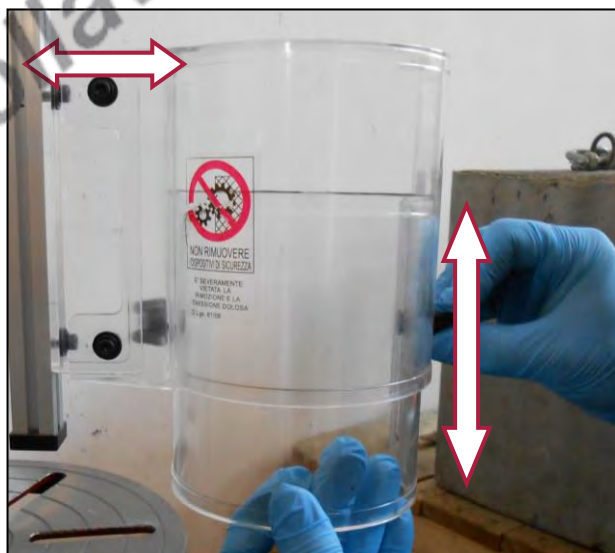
Scorrimenti del riparo in senso verticale e longitudinale
